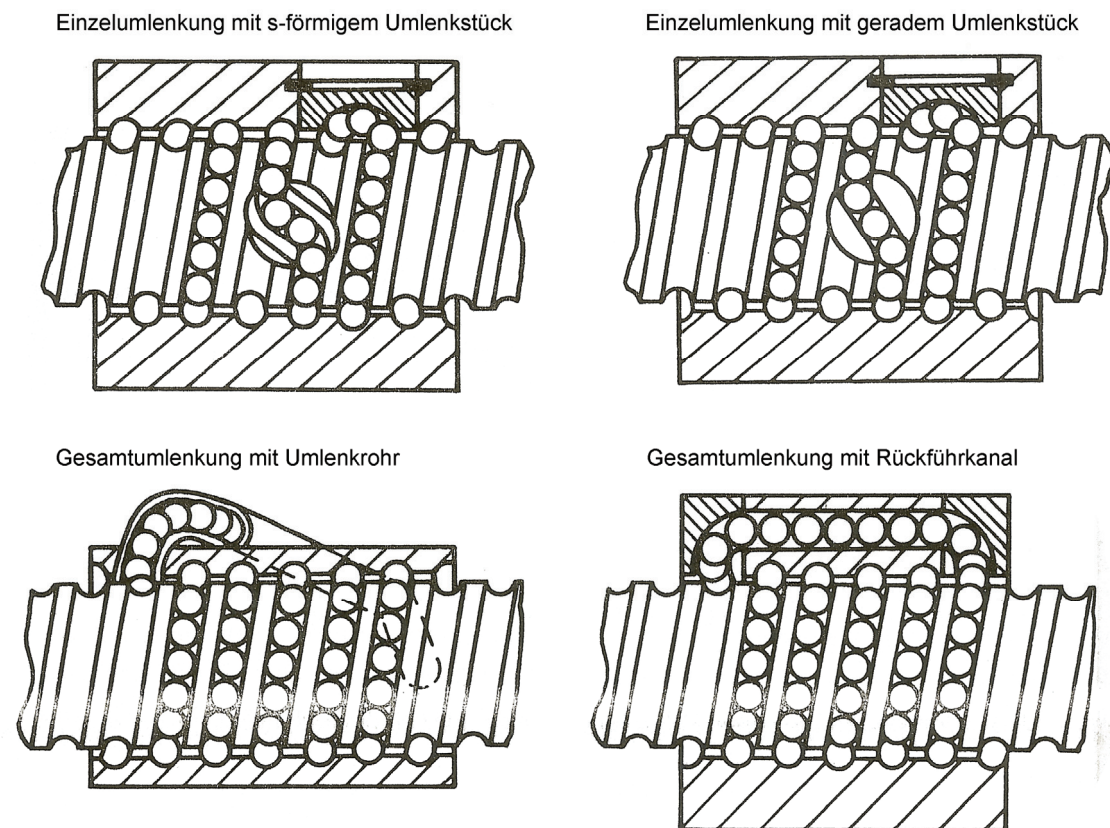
Bauformen der Kugelrückführung [Go90]
